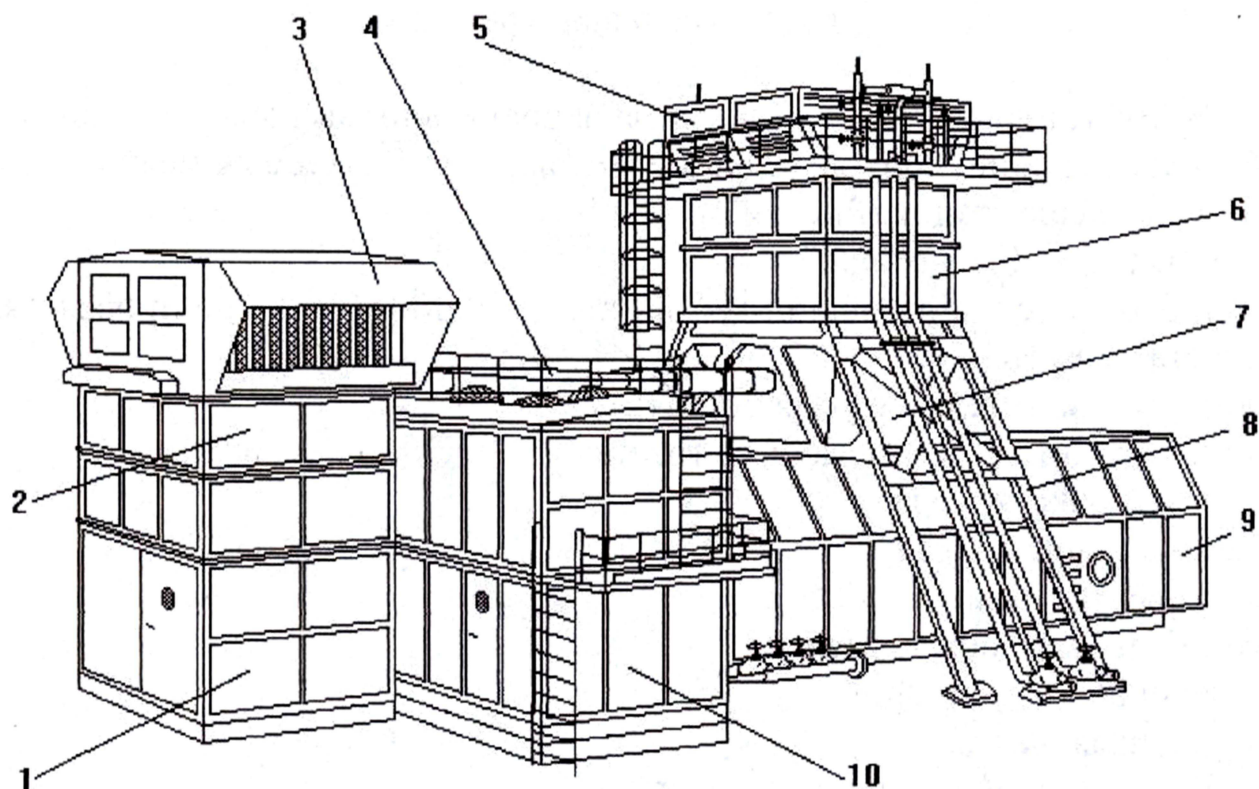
Общий вид газоперекачивающего агрегата ГПА-Ц-16:
